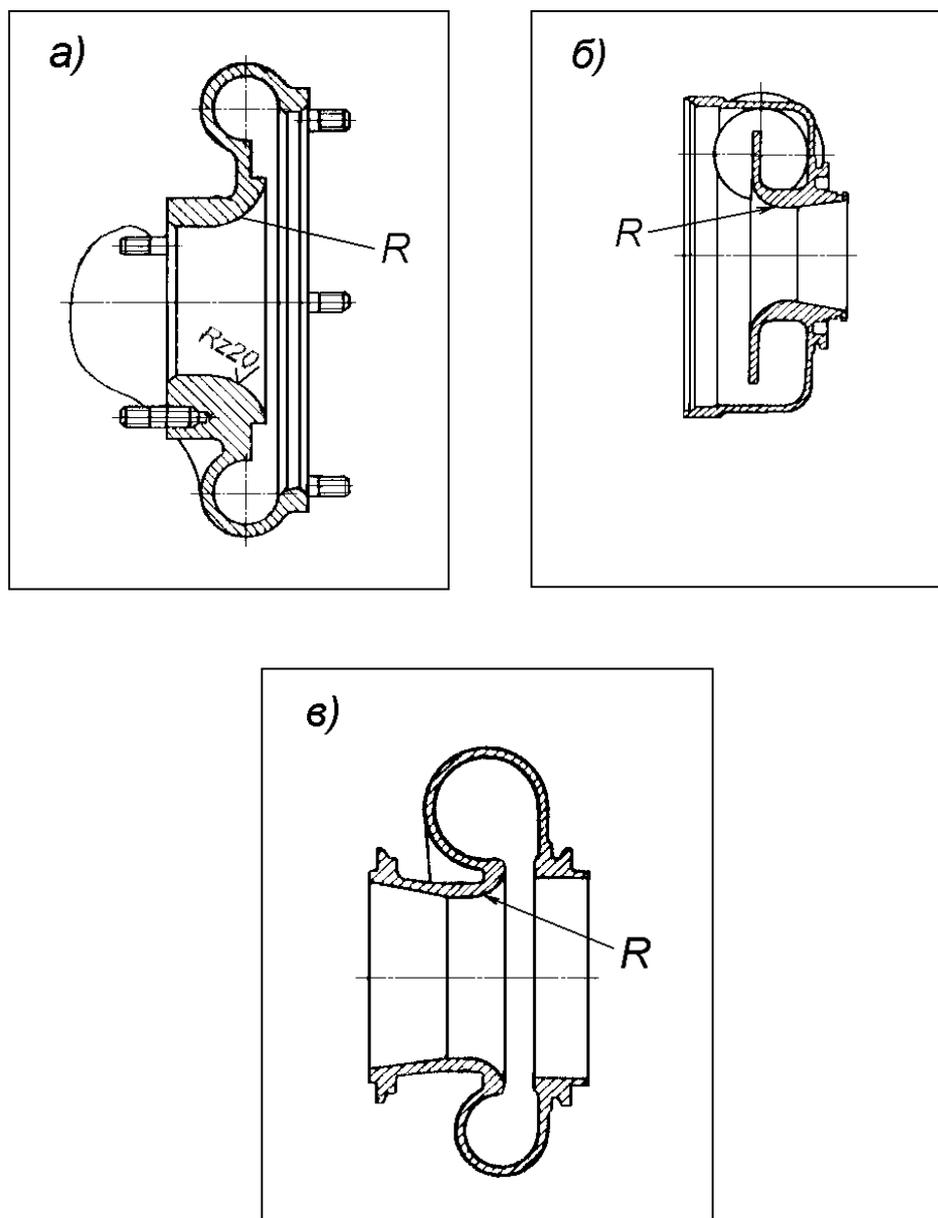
а) – корпус компрессора ТКР-11 ЯМЗ; б) – корпус компрессора ТКР-9 ЯМЗ;
